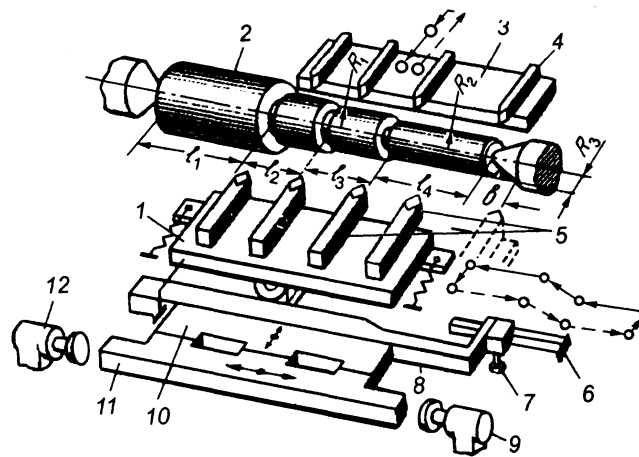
Схемы выставки резцов на многорезцовом полуавтомате: 1 — продольный суппорт; 2 — деталь (эталон); 3 — резцедержатель; 4, 5 — резцы; 6 — планка; 7 — винт; 8 — линейка; 9 — регулировочный винт; 10 — выступ верхней линейки; 11 — нижняя линейка; 12 — упор
